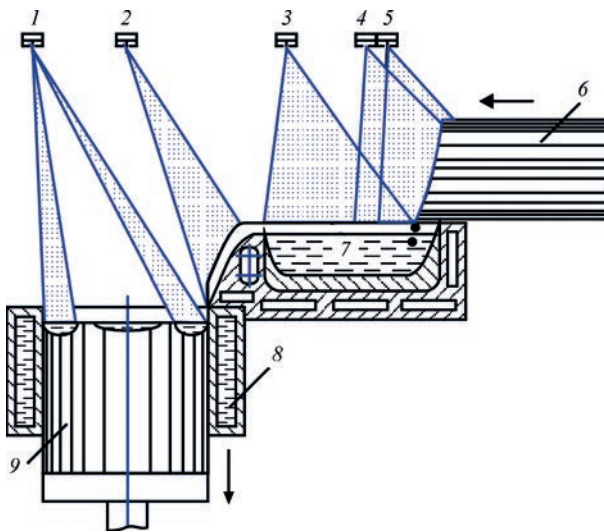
Схема електронно-променевої плавки з проміжної ємності: 1–5 — електронно-променеві гармати; 6 — витратна шихтова заготовка; 7 — проміжна ємність; 8 — кристалізатор; 9 — зливковий
